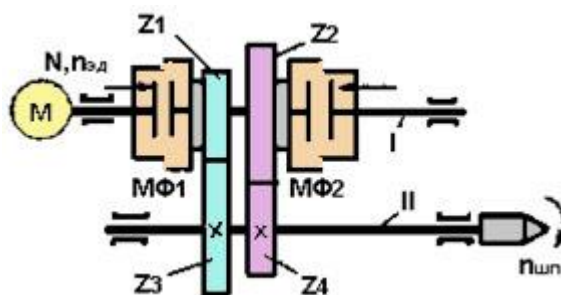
Регулирование с помощью зубчатых колес и муфт.
